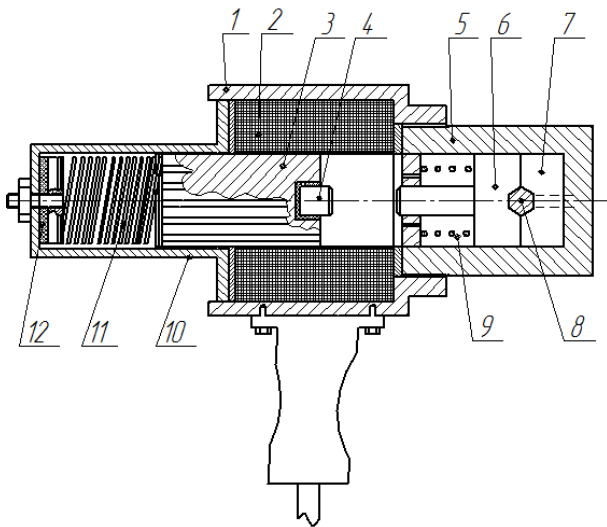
Схема низкочастотной ручной ударной машины с энергией удара 40-50 Дж: 1 – корпус; 2 – электромагнитная катушка; 3 – боек; 4 – ударник; 5 – матрицедержатель; 6 – пуансон; 7 – матрица; 8 – обрабатываемое изделие; 9 – поджимающая пружина; 10 – корпус возвратного механизма; 11 – возвратная пружина; 12 – вибродемпфер
